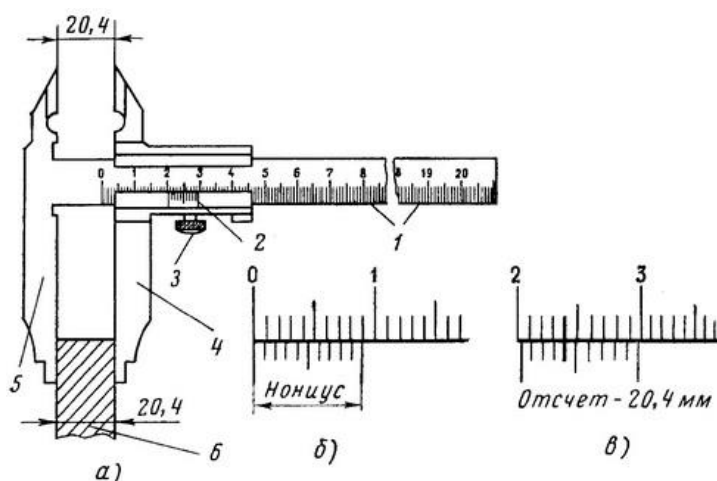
Чтение показаний на штангенциркуле по шкалам штанги и нониуса: а- штангенциркуль ШЦ-II; б – шкала нониуса; в – пример чтения показаний
